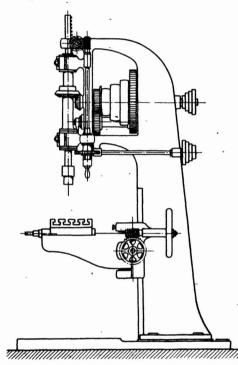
Vertikalbohrmaschine mit Hohlgußgestell.
